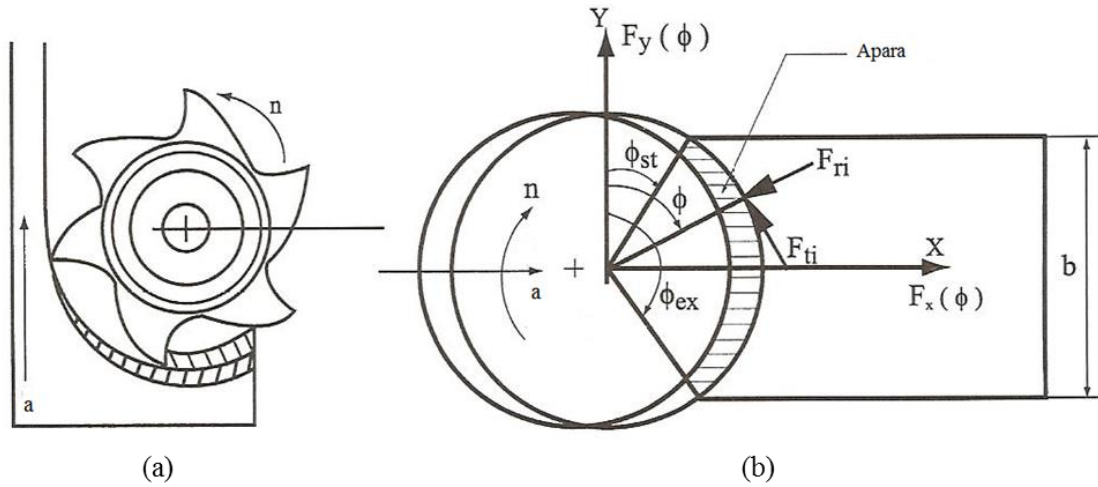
Movimentos de corte: (a) Movimentos de avanço e rotação da ferramenta; (b) Geometria da fresagem, ângulos de entrada, saída e de imersão [12].
